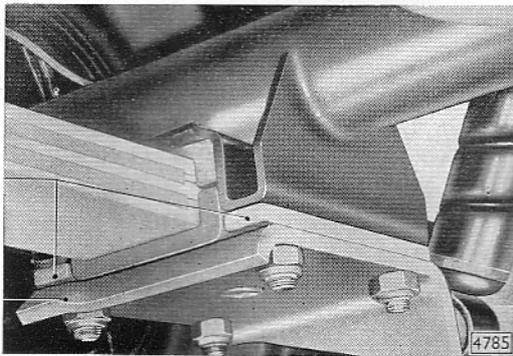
Befestigung Hinterachse an Hinterfeder
